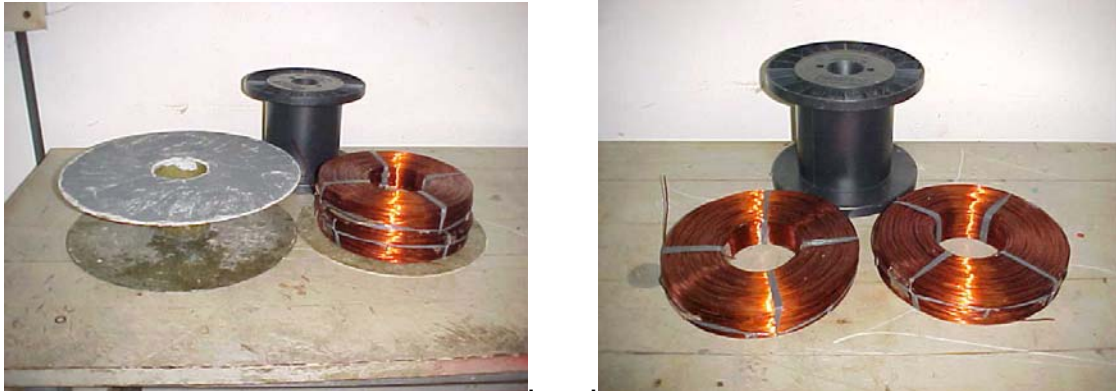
Fotos das bobinas montadas e do carretel de fibra. O carretel preto trouxe o fio enrolado.
